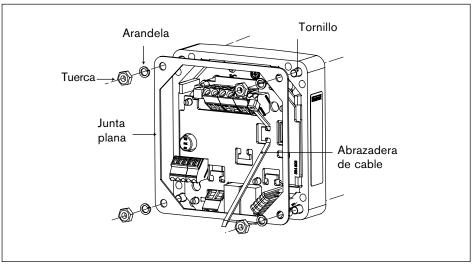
Instalación de la versión de montaje en panel del modelo 8025
